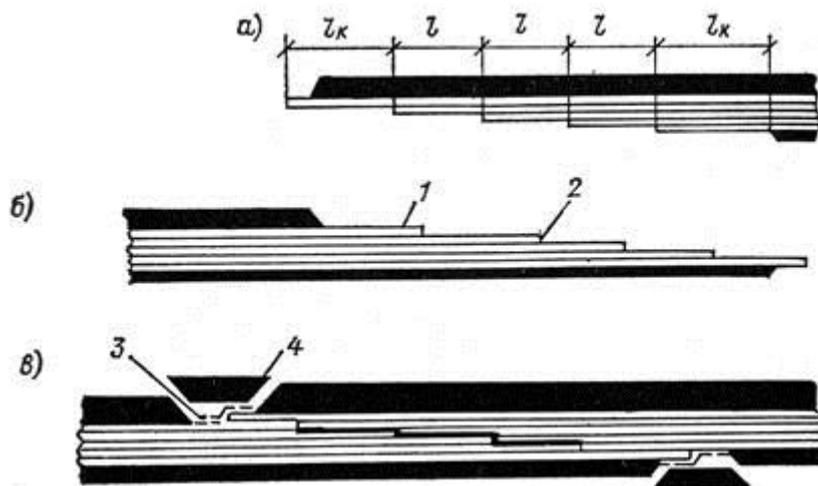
Подготовка стыка при вулканизации: а, б – схемы наложения разделочной резины; в – заделки в стыке ленты; 1 – прослоечная резина; 2 – полоски резины; 3 – бреккерная ткань; 4 – резиновая заготовка (заделка)
